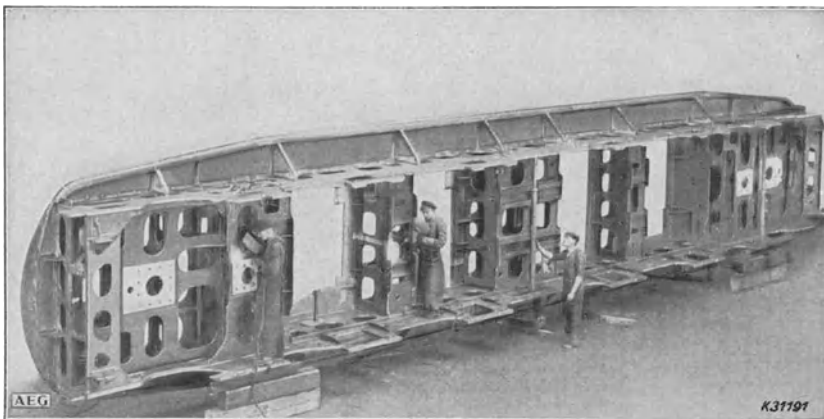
Geschweißter Lokomotivrahmen.
